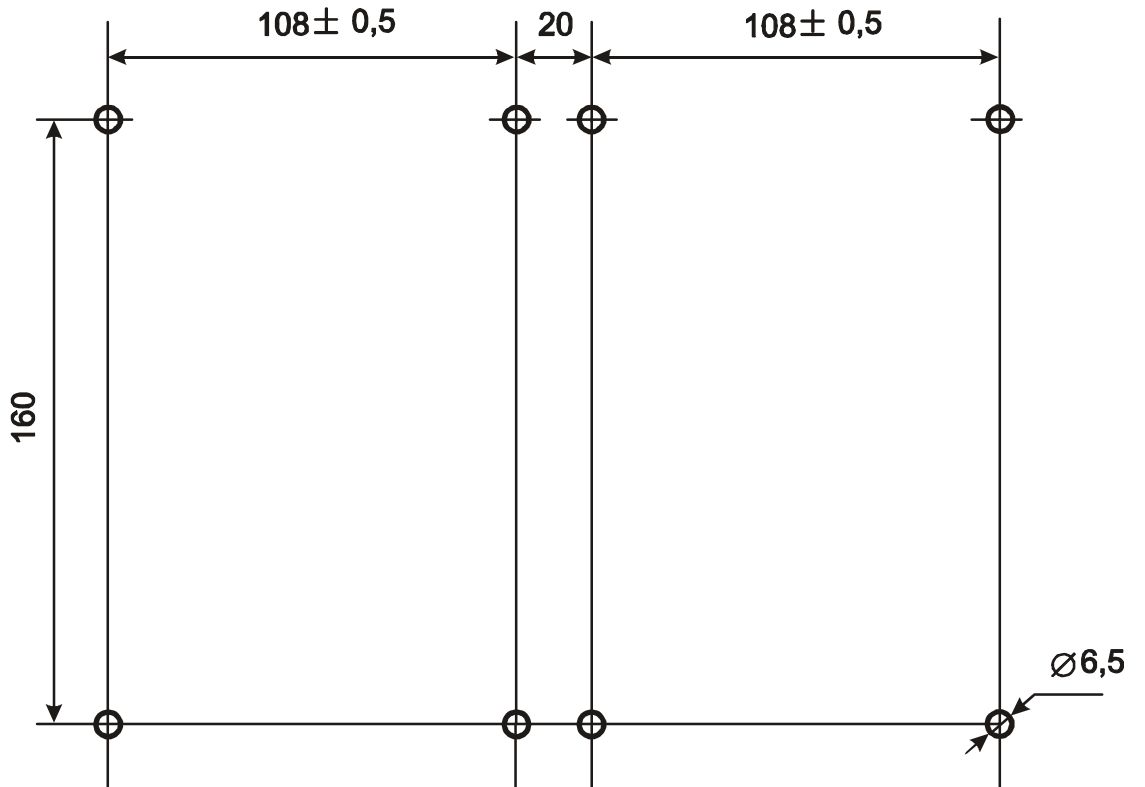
а – Разметка для групповой установки ИП-40030-0-0-В4,
